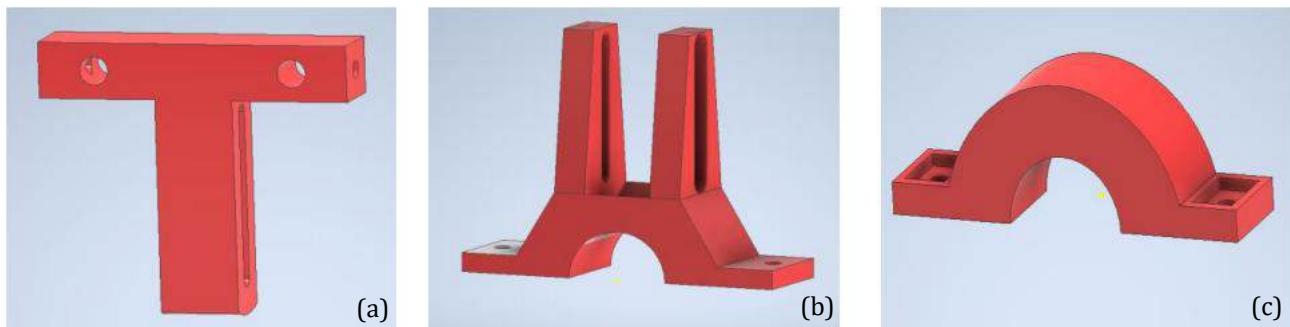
SUPORTE DO MOTOR DE PASSO.
